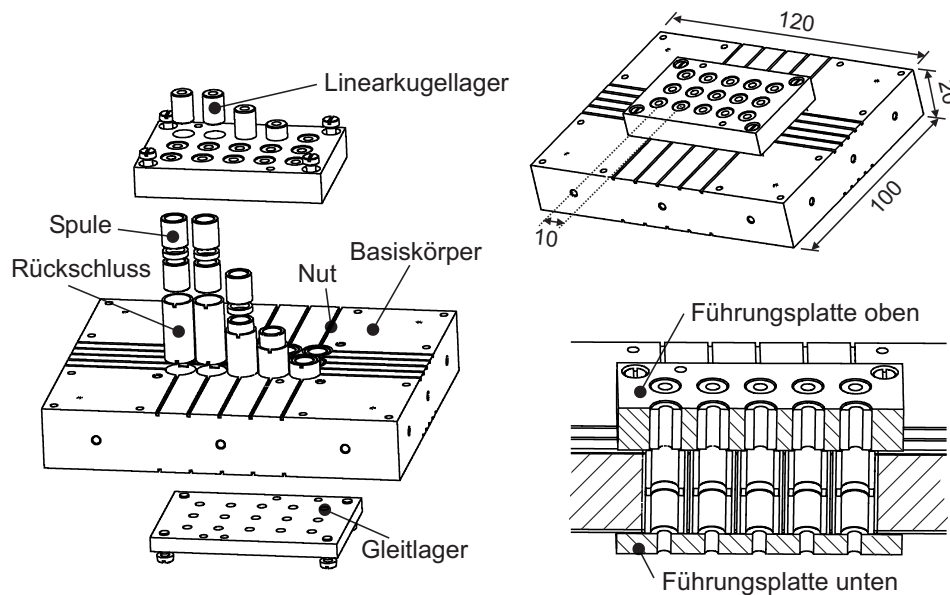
Der Stator im zusammengebauten Zustand, im Schnitt und als Explosionszeichnung.
